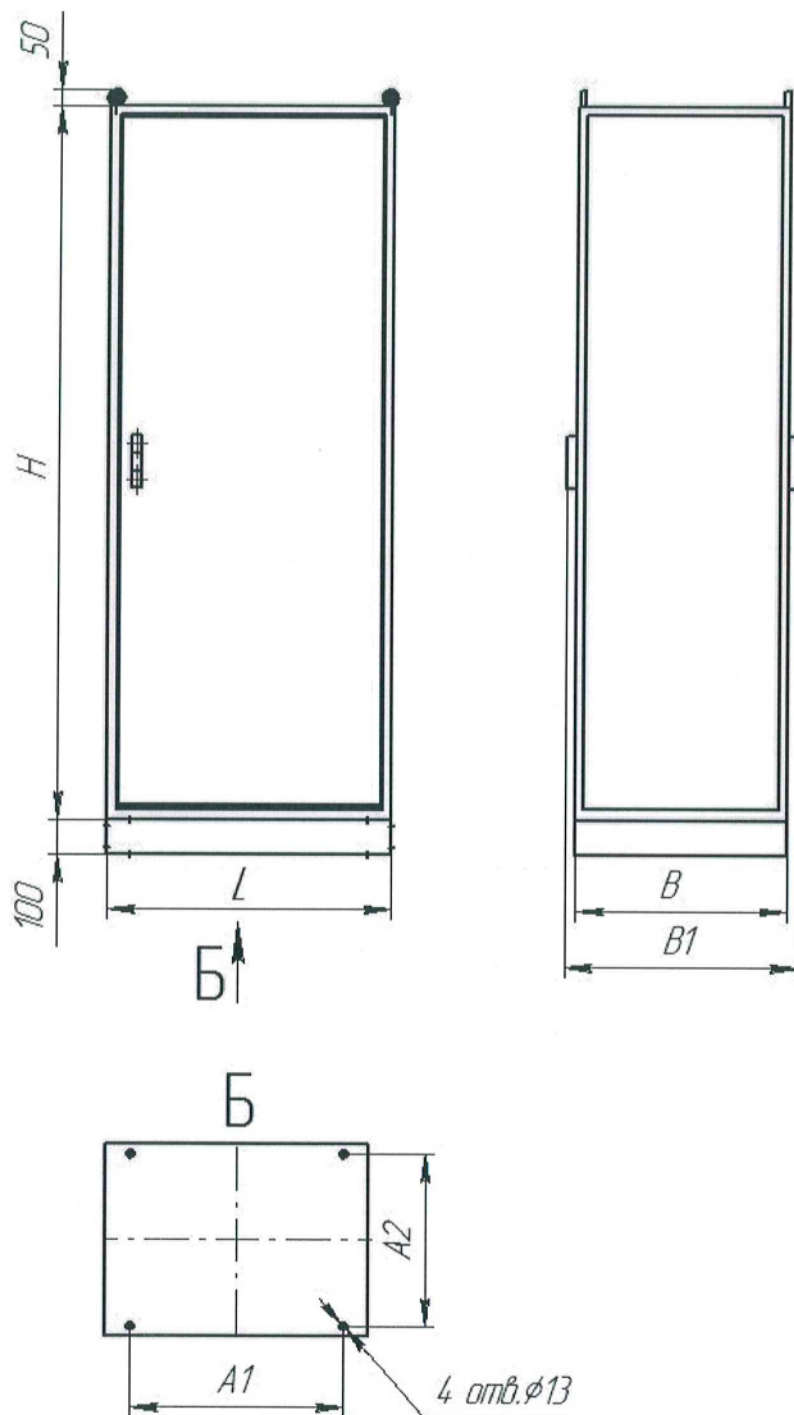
Габаритные и установочные размеры шкафа с одним цоколем
